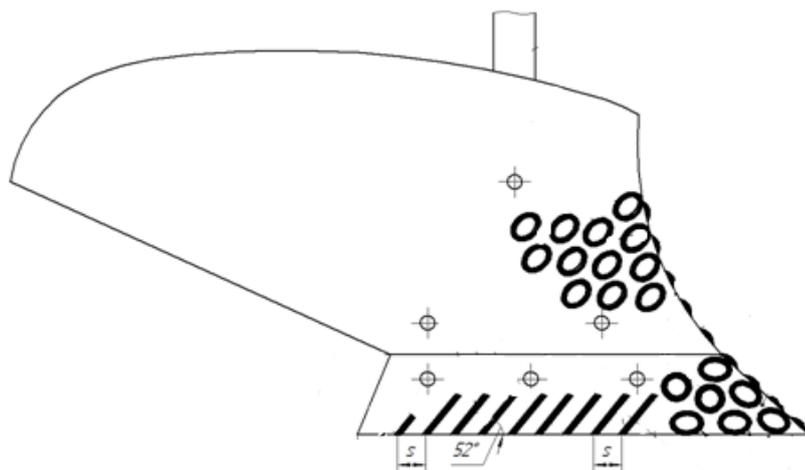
Расположение прямолинейных и кольцевых валиков твердого сплава в зонах наибольшей интенсивности трения лемешно-отвальной поверхности корпуса плуга с уплотненной почвой [7,8]
